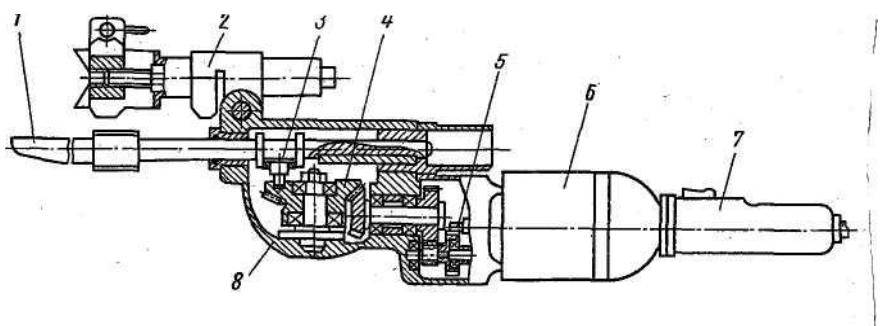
Ножовка ОЭС-840. Общий вид
